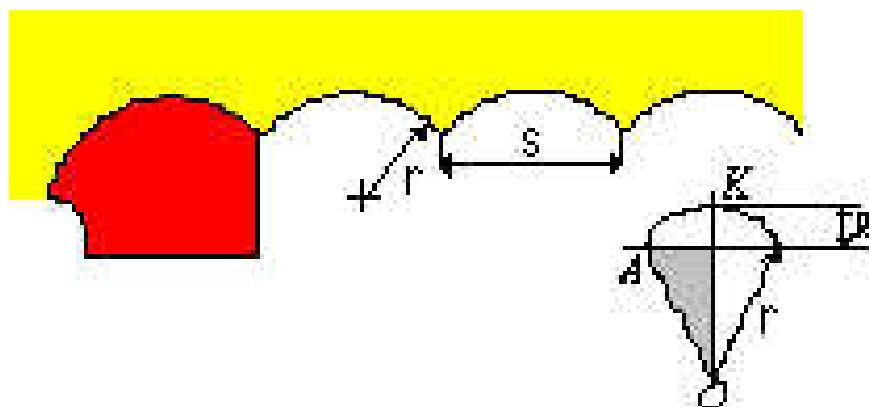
Схема обработки резцом с радиусной вершиной
